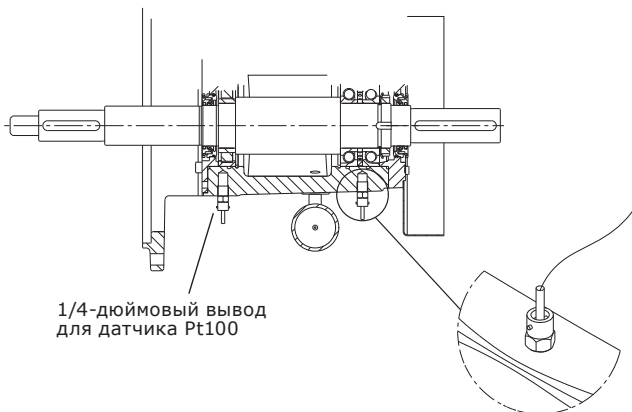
Датчики Pt100, установленные в корпус подшипников
